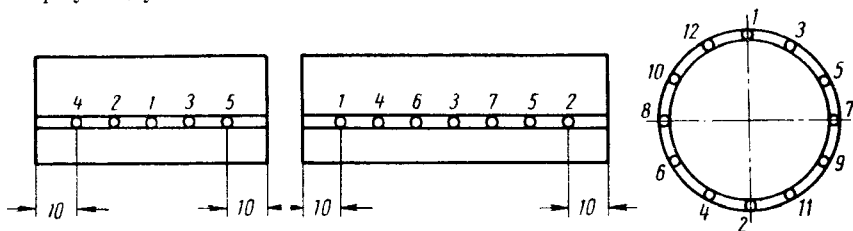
Порядок наложения прихваток (1—12) перед сваркой латуни
